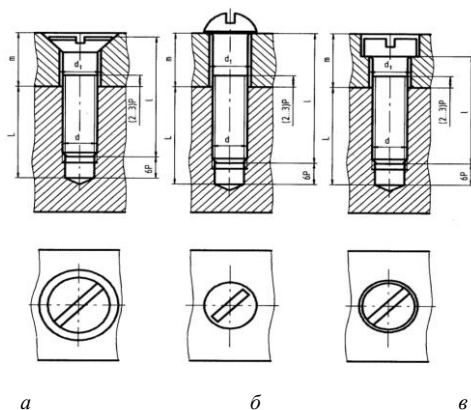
Соединение деталей винтом: а – винт с потайной головкой; б – винт с полукруглой головкой; в – винт с цилиндрической головкой
